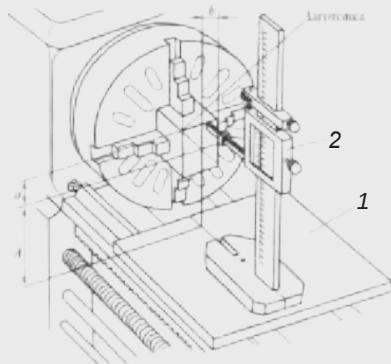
Закріплення та вивірка заготовки за допомогою штангенрейсмуса: *1* — плита; *2* — штангенрейсмус; *А, а, b* — розміри, які визначають штангенрейсмусом
